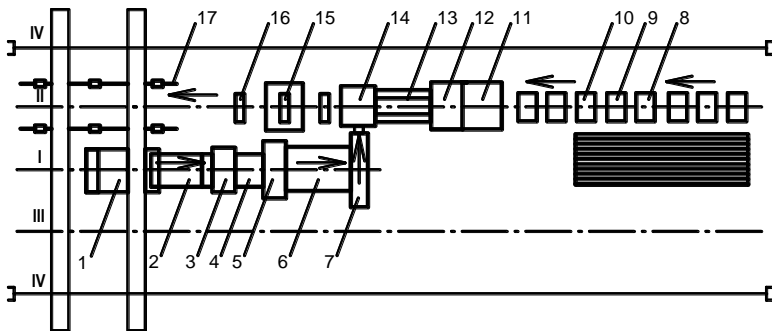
Схема полуавтоматической поточной звеносборочной линии ЗЛХ-800: 1 – подвижный склад шпал; 2 – приемный конвейер; 3 – шпалопитатель; 4 – шаговый конвейер; 5 – сверлильный станок; 6 – накопитель; 7 – шпальный поперечный конвейер; 8 – рельсовый рольганг; 9, 10 – упоры; 11, 12 – бункера для скреплений; 13 – питатели; 14 – сборочный агрегат; 15 – приемная рама, 16 – тележки, 17 – перегружатель
